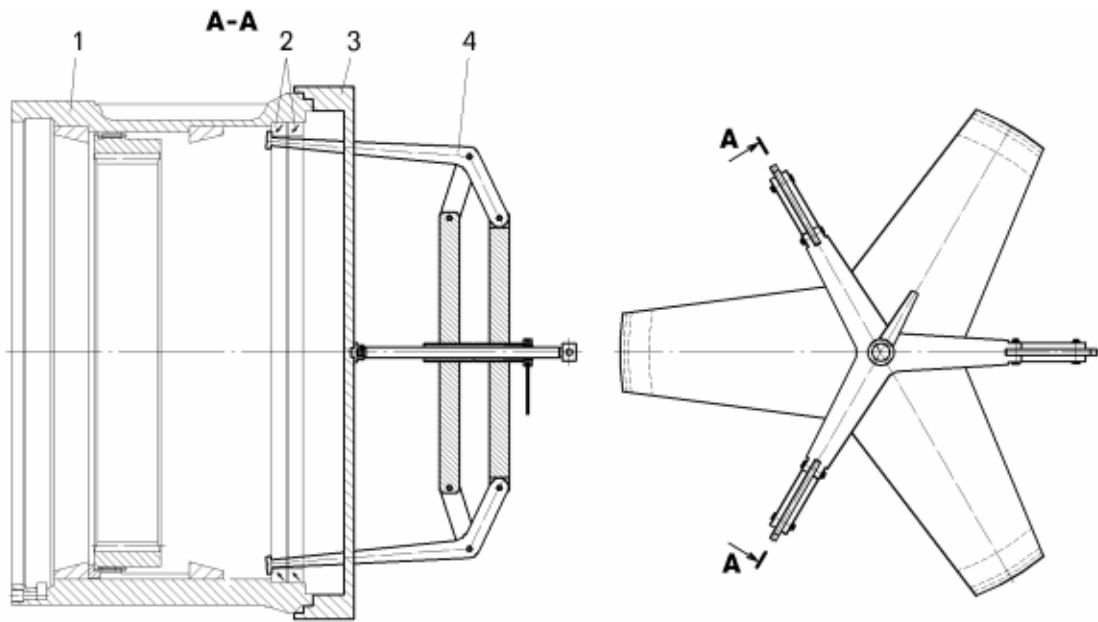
Приспособление для снятия манжеты из ступицы мотор-колеса:
